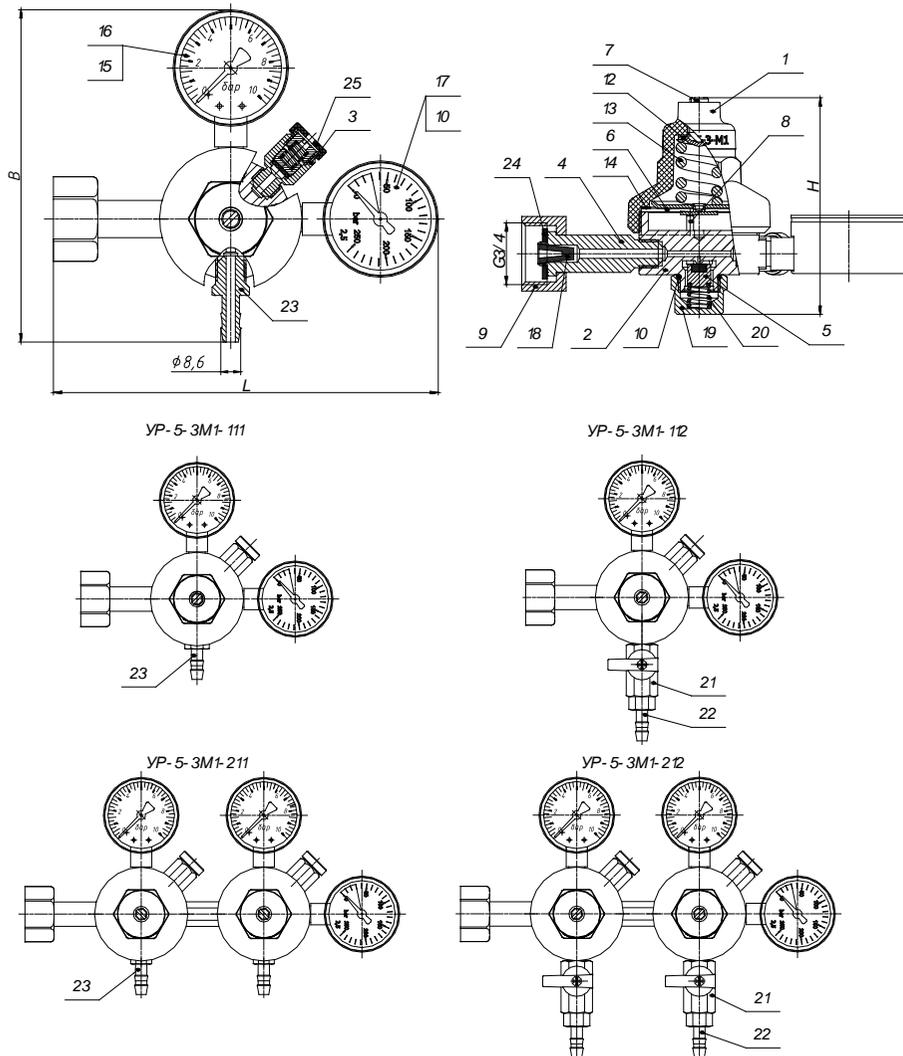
Редуктор баллонный углекислотный одноступенчатый.
